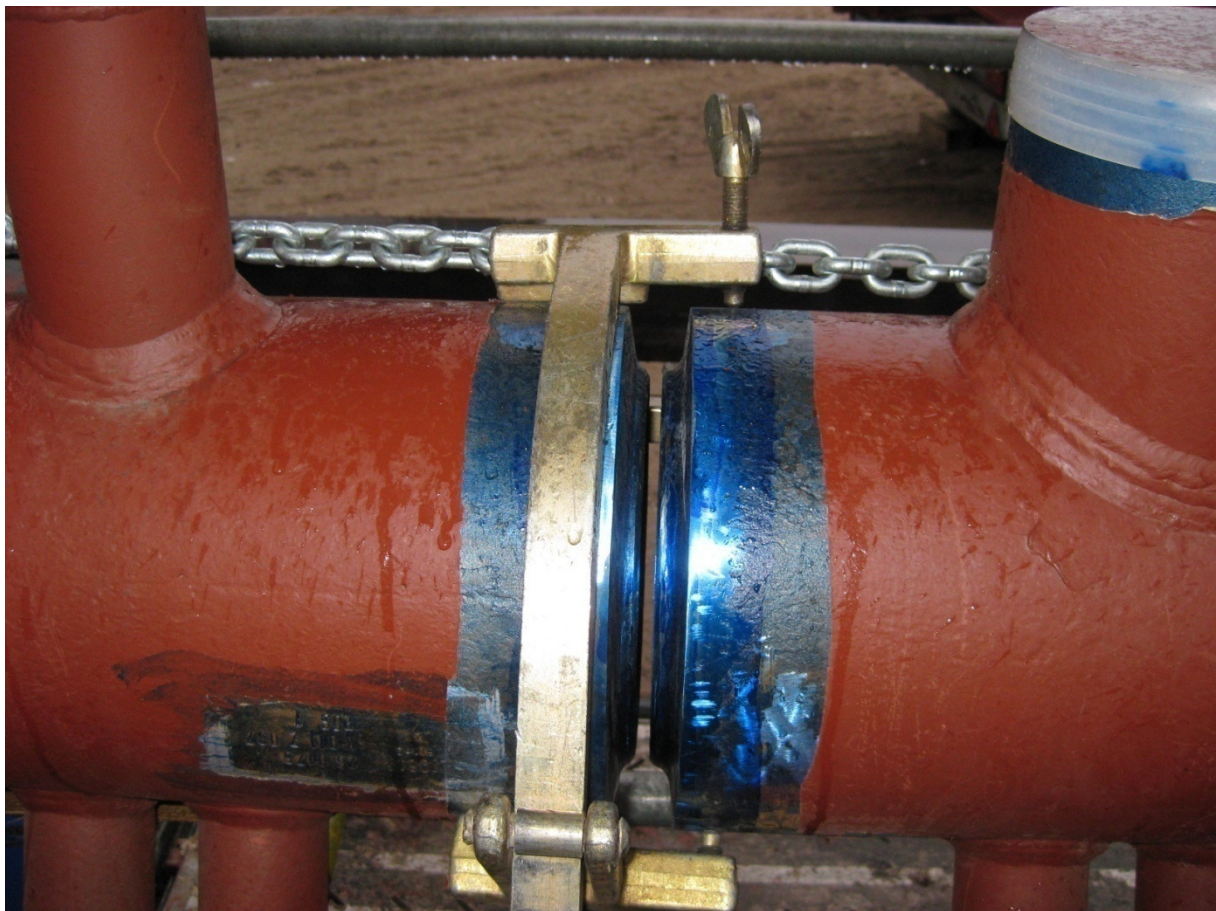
Vorbereitung einer Heftschweißung eines Sammlers
